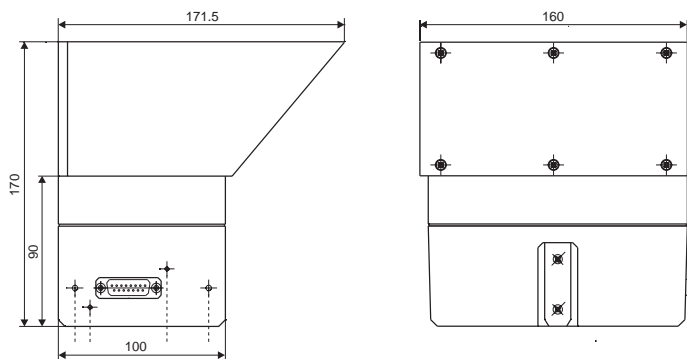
Maßzeichnung BCL 80 mit Schwenkspiegelaufsatz
